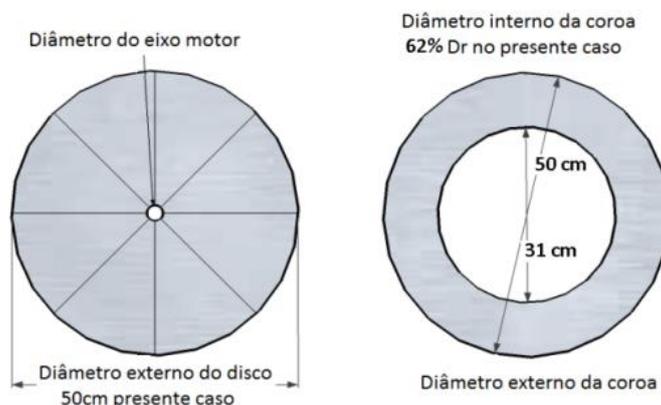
Detalhes do disco principal, destacando-se os locais para assentamento das pás e do anel externo do rotor ou coroa.
